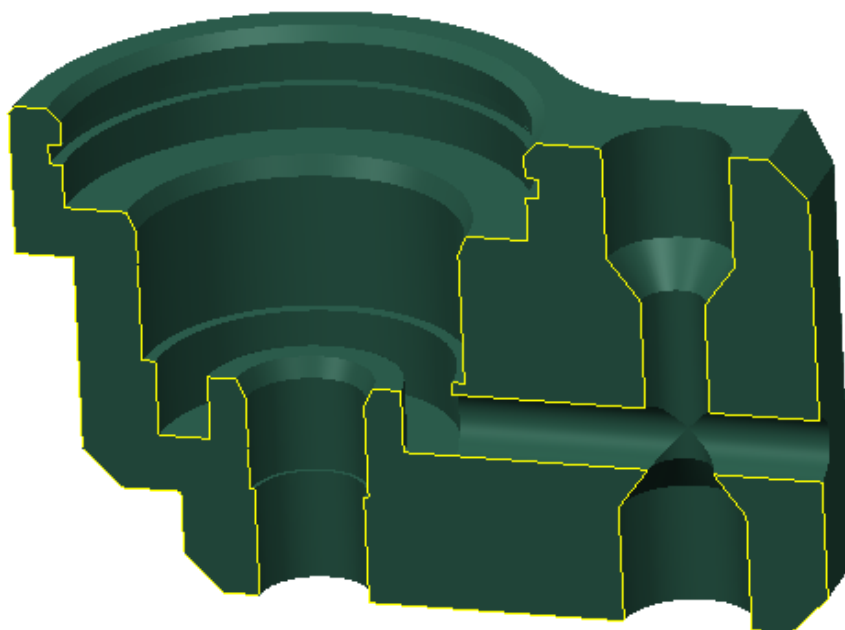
Regulátor tlaku paliva Bosch MINI A [30]
